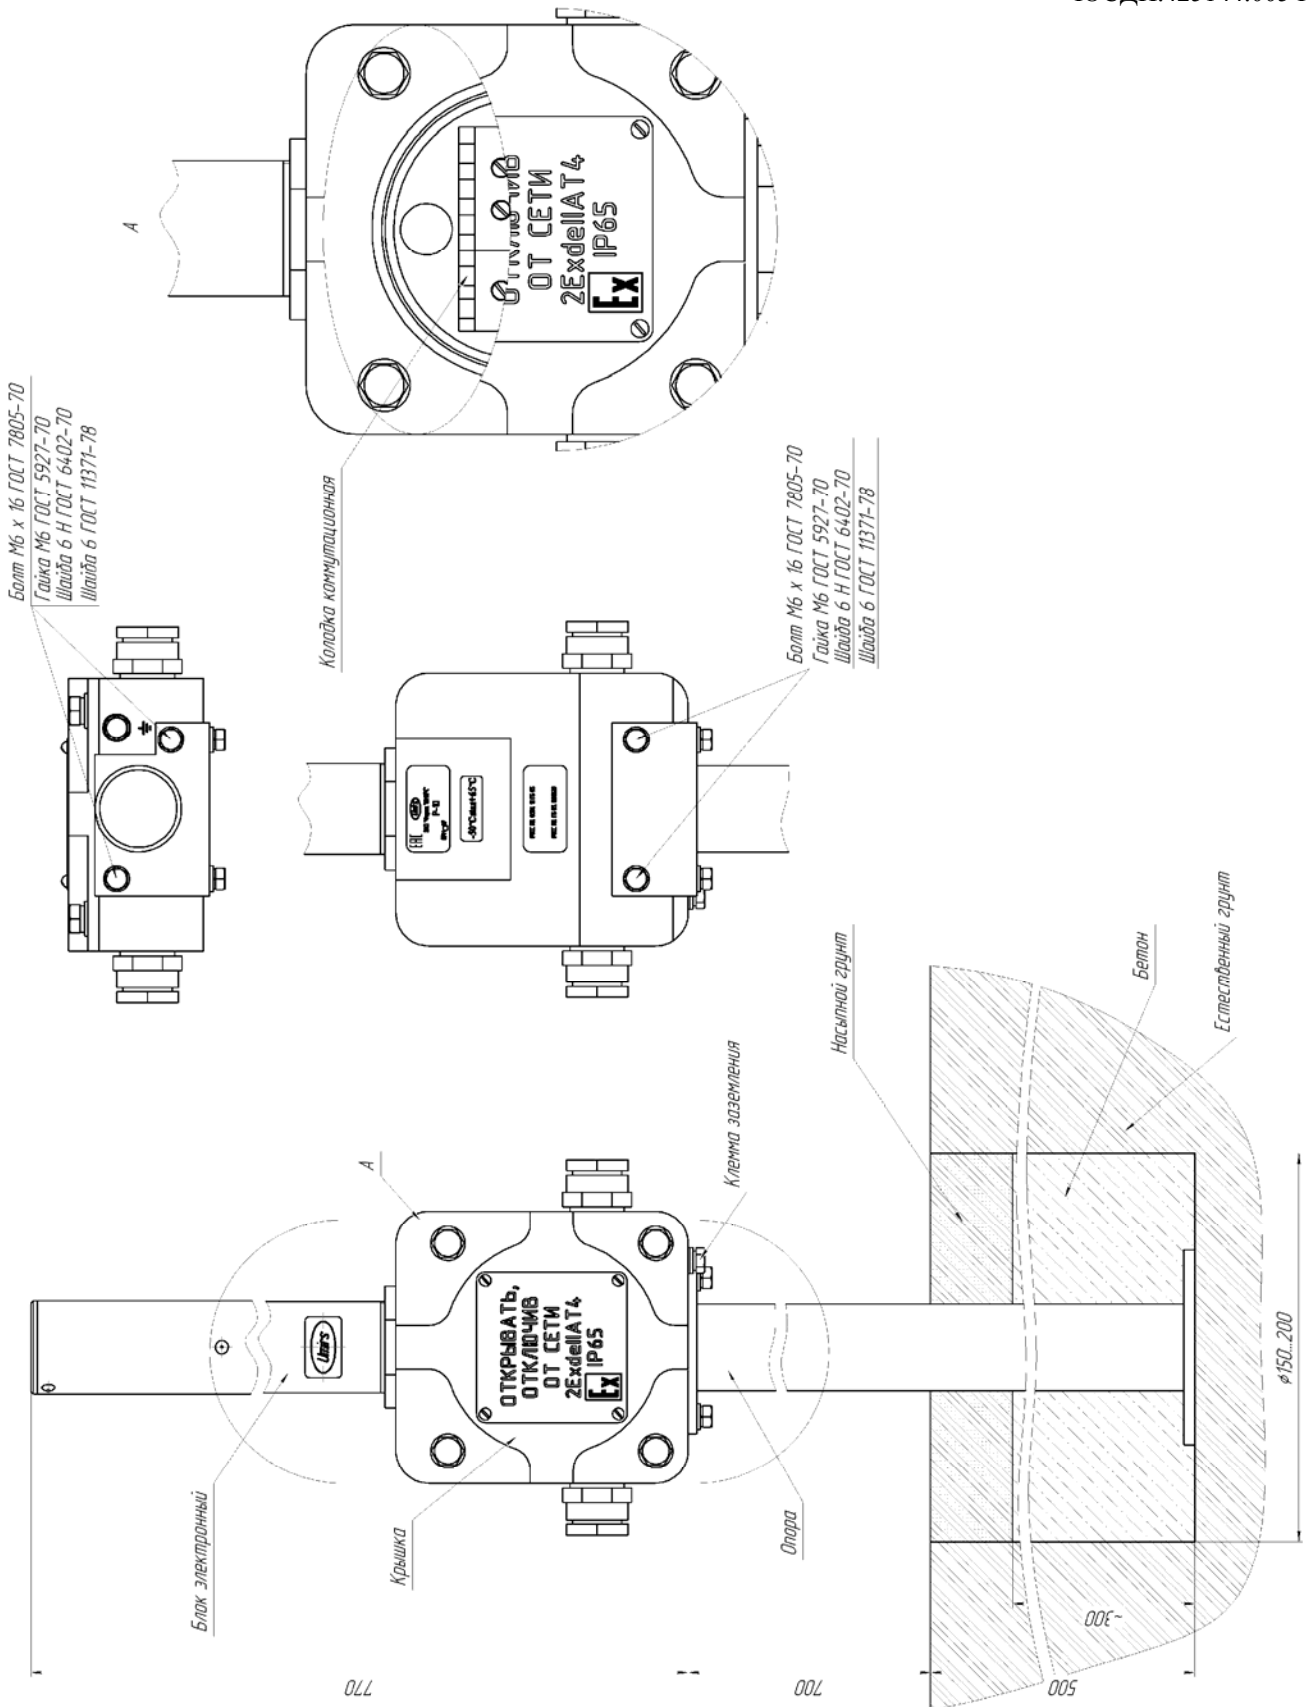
Внешний вид ПРМ, закрепленного на опоре
